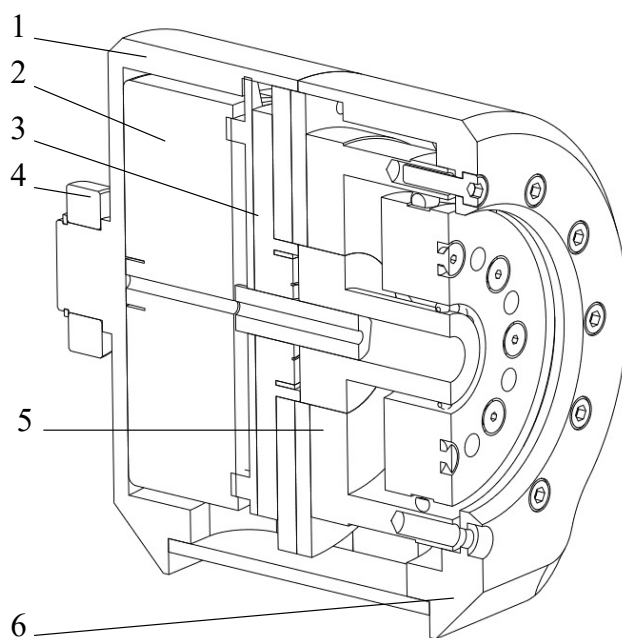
Внешний вид коленного шарнира экзоскелетного комплекса
